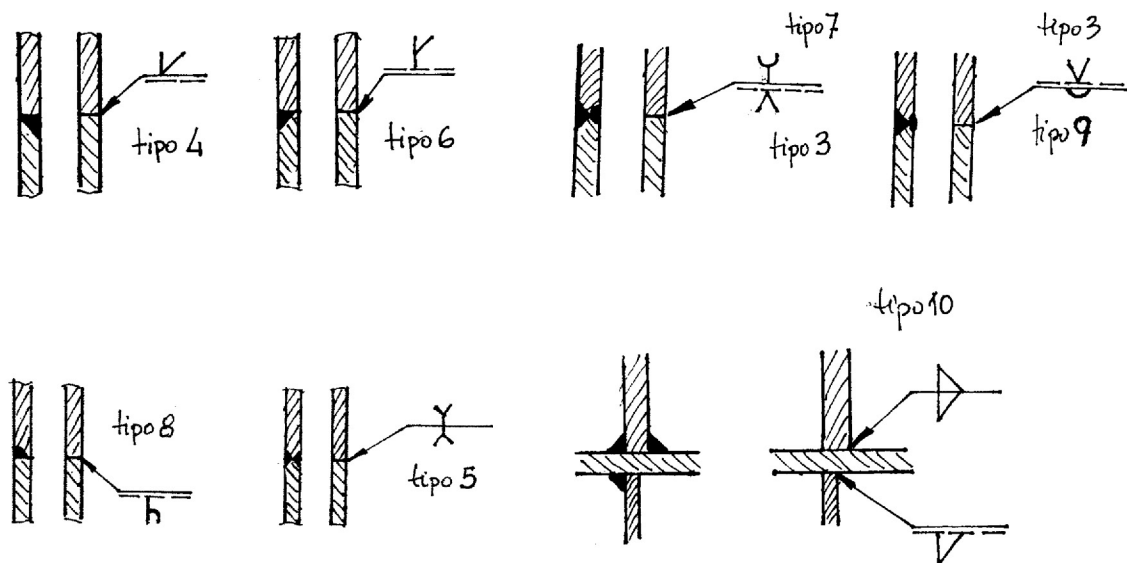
Ejemplos de representación normal y simbólica de diferentes posiciones del cordón de soldadura (con indicación del tipo de soldadura, según la tabla 2.2)
